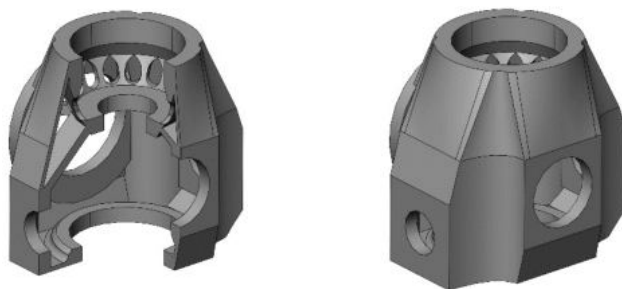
Общий вид и сечения адаптированного под 3D-печать корпуса компрессора
